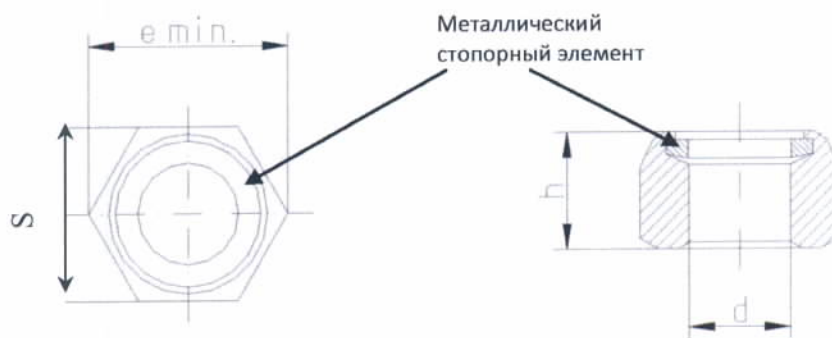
Конструкция и обозначение геометрических размеров FS-гайки
